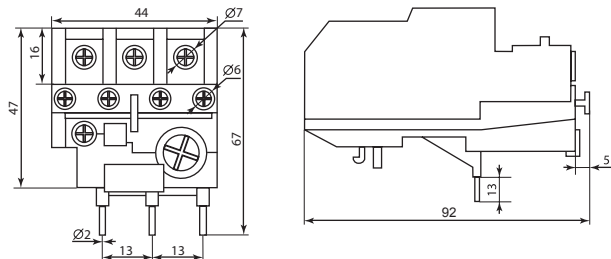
Габаритные и установочные размеры реле РТЛУ-1001-М2...РТЛУ-1022-М2
